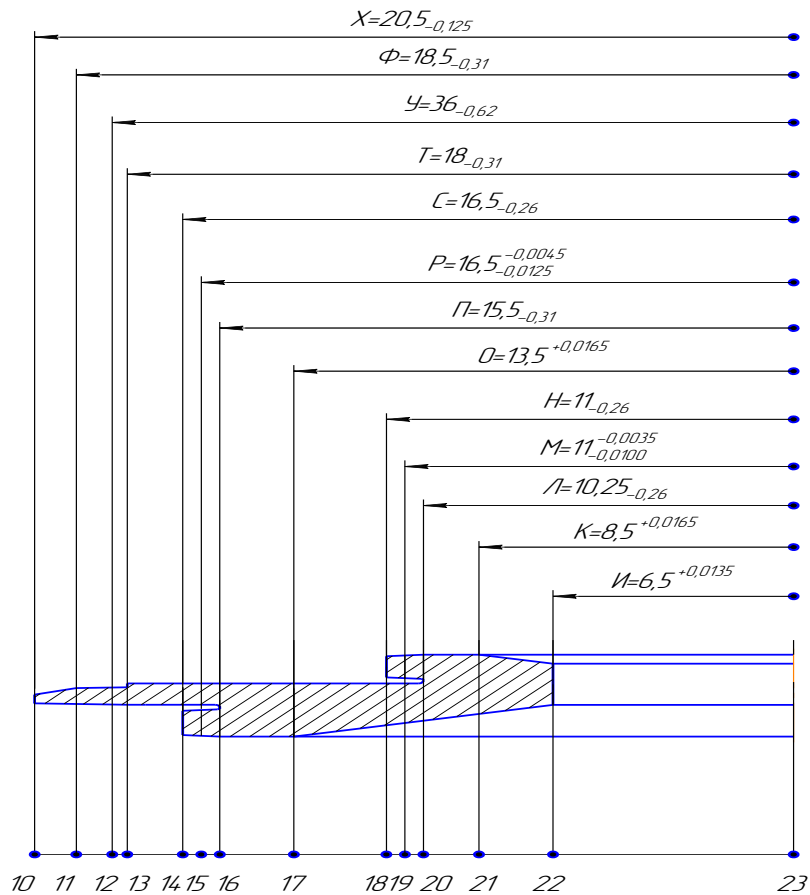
Преобразованный чертеж базовой детали на ось OZ
